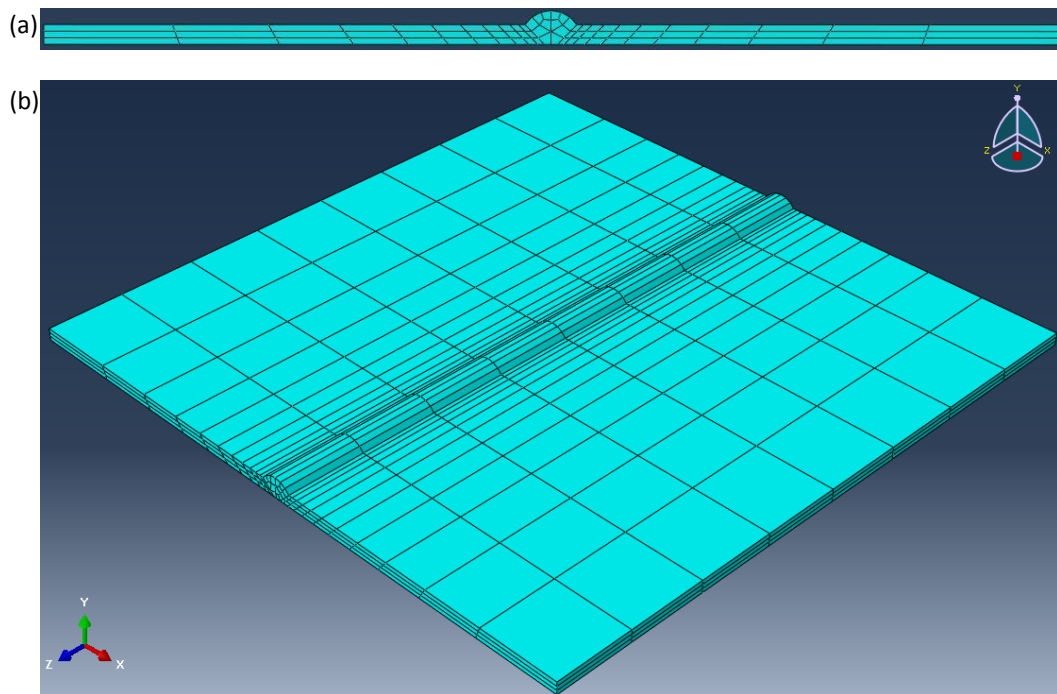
Mallado utilizado en junta con placas de 76.2 mm de ancho: (a) Vista frontal de la junta y (b) Modelo 3D.
